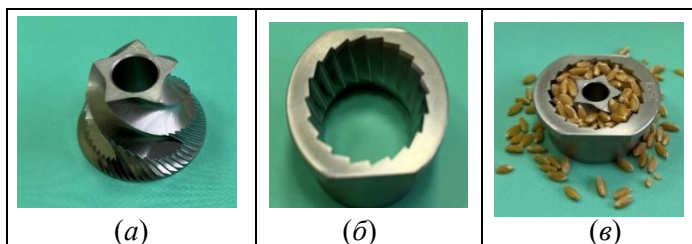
Рабочие органы измельчителя: подвижный валец (а); неподвижный кольцеобразный «валец» (б) и их расположение в конструкции измельчителя (в)
